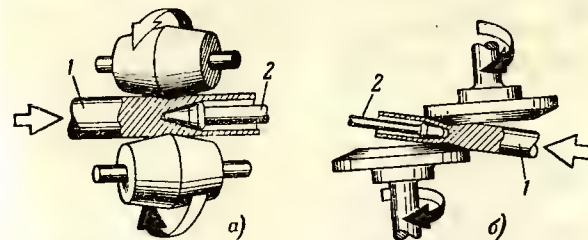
Схемы прошивки заготовки цельнотянутой трубы.
